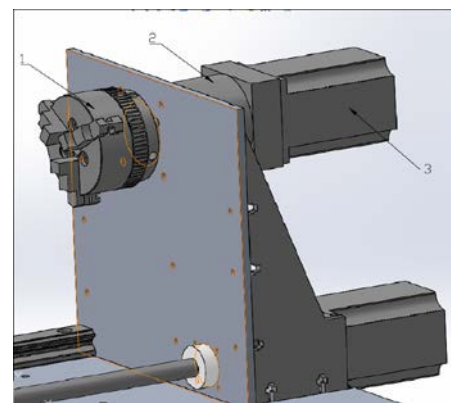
Передняя бабка: 1 - шпиндель; 2 - редуктор; 3 - шаговый двигатель
